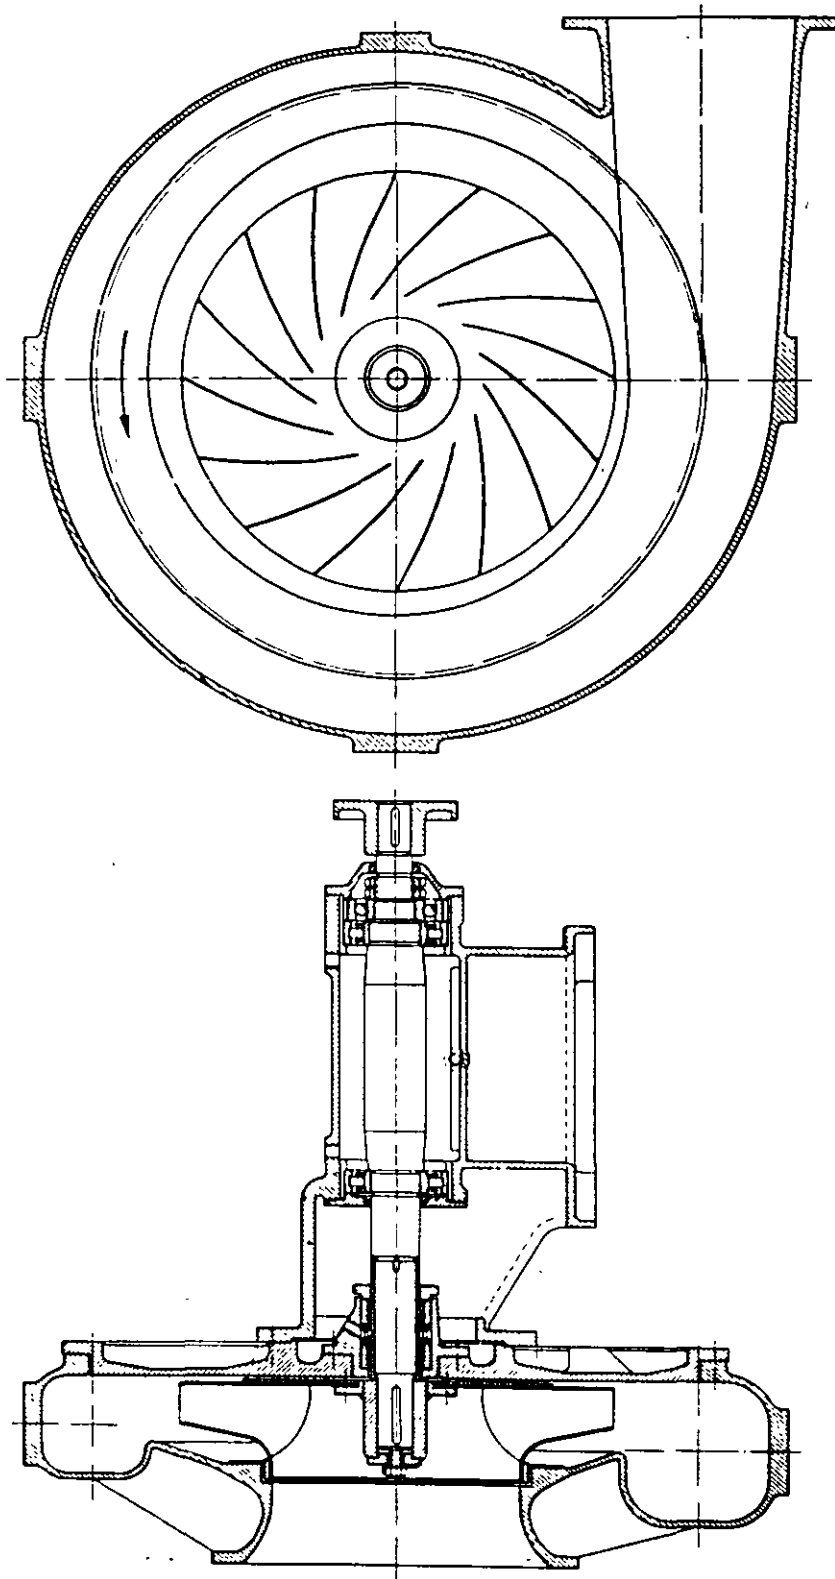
Ventilador de alta presión construido por la casa Sulzer para 2.950 rpm con un caudal de 16.000 m³ h y una presión de 70 mbar con un diámetro exterior del rodete de 700 mm.
